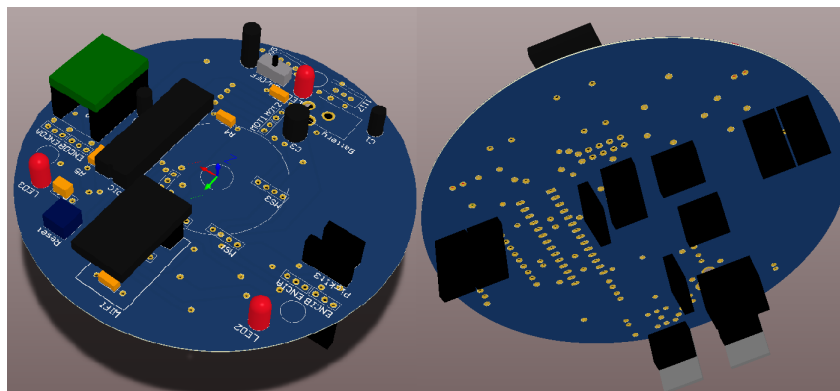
A la izquierda, vista superior simulada de la placa con componentes.
